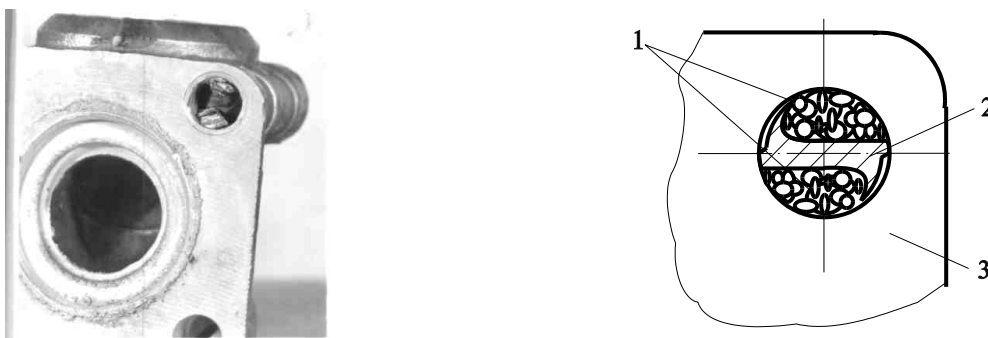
Характерна поломка гвинтового свердла $\varnothing 11,2$ мм в корпусних деталі через пакетування стружки в стружкових канавках (матеріал заготовки АК7, інструменту Р6М5Ф3, $V = 31,38$ мм/хв., $S = 0,26$ мм/об., охолодження Аквол 10-М 5...7 л/хв.
